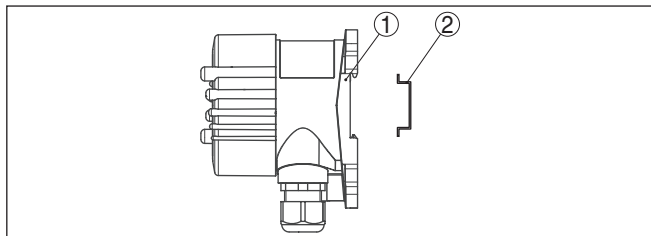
VEGADIS 81 с пластиковым корпусом для монтажа на несущей рейке
